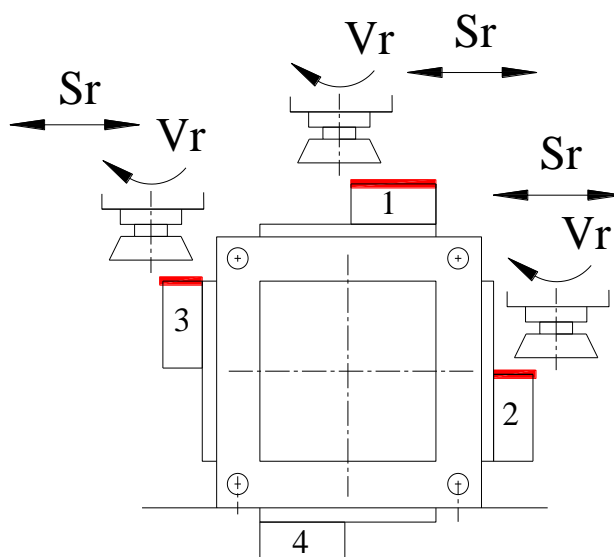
Эскиз наладки для варианта обработки трех деталей на спутнике призматической формы.
